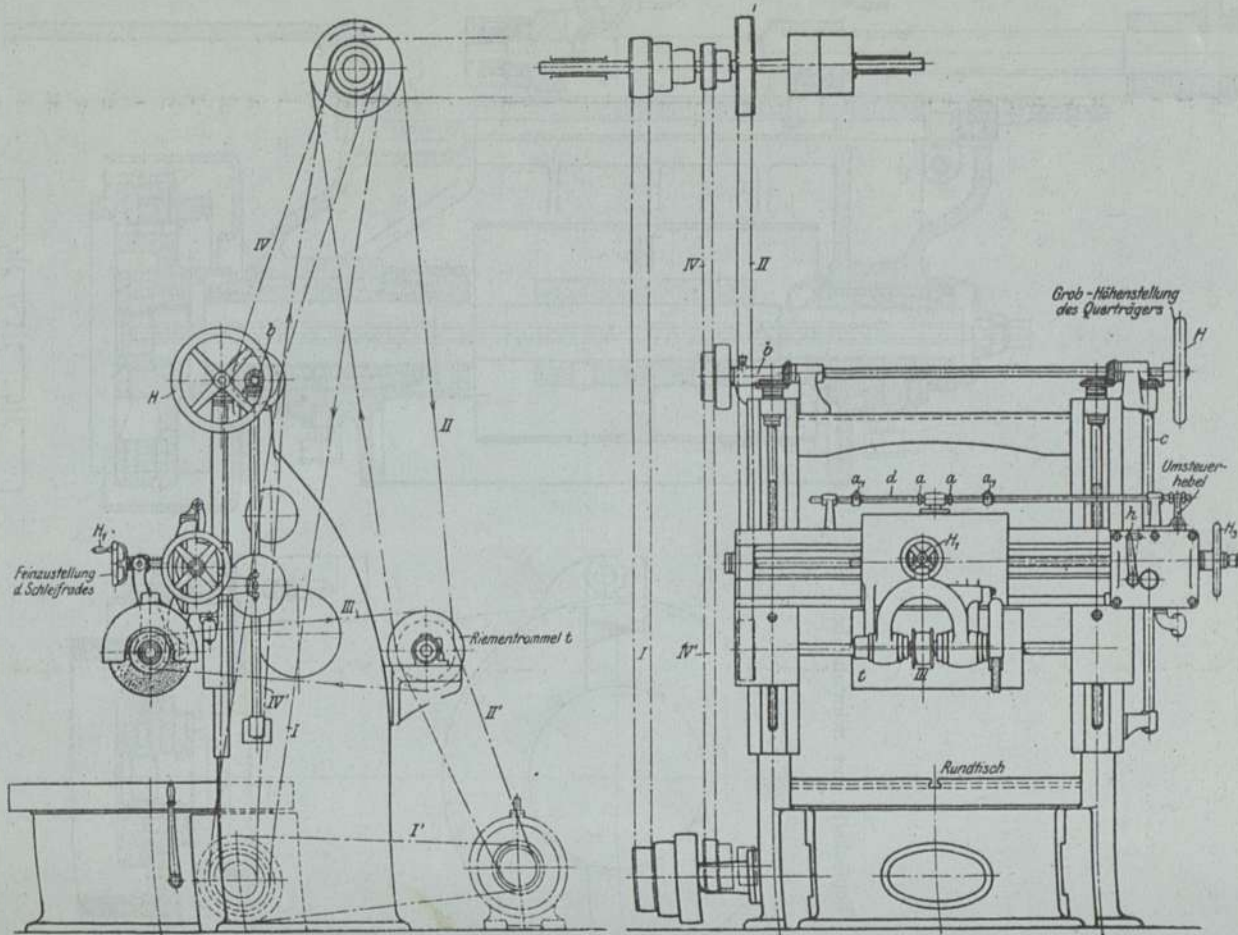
und 709. Planschleifmaschine für Ringflächen. Fr. Schmaltz, G. m. b. H., Offenbach/M.
